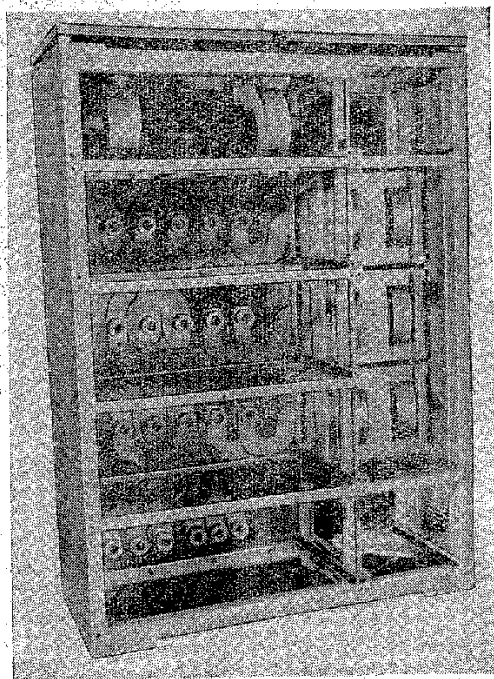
Каркас агрегата блочной конструкции в сборе.
